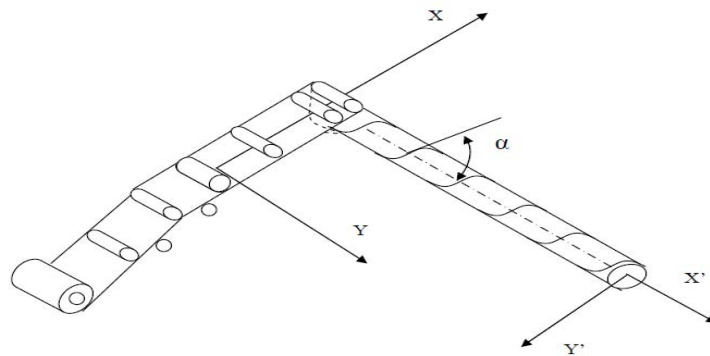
Principe de fabrication des tubes soudés en spirale.
